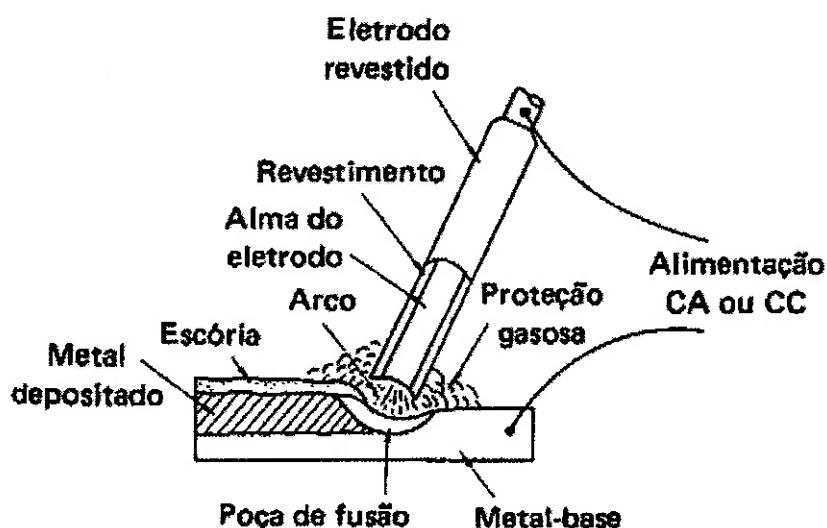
Esquema da soldagem com o processo Eletrodo Revestido [22].
